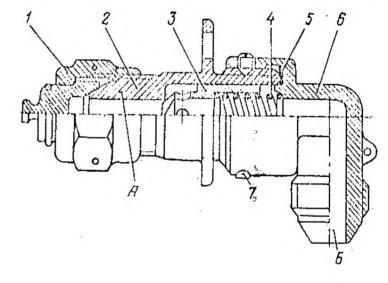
Бортовой клапан подключения наземной гидроустановки
